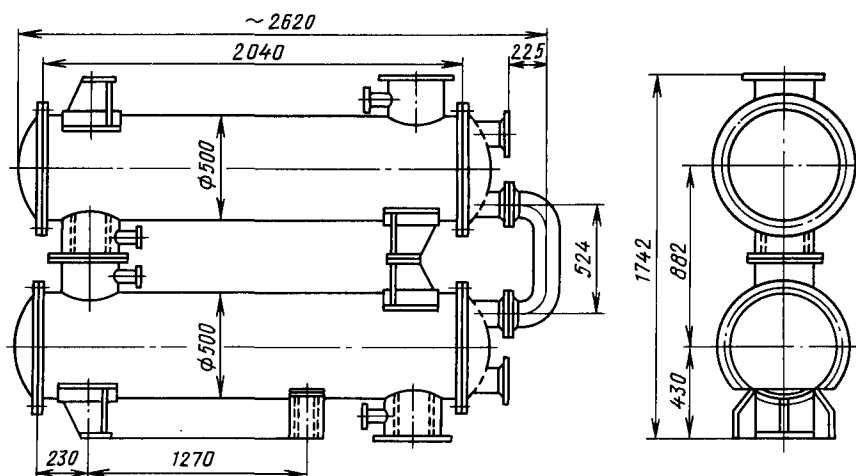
Блок из двух кожухотрубчатых теплообменников
